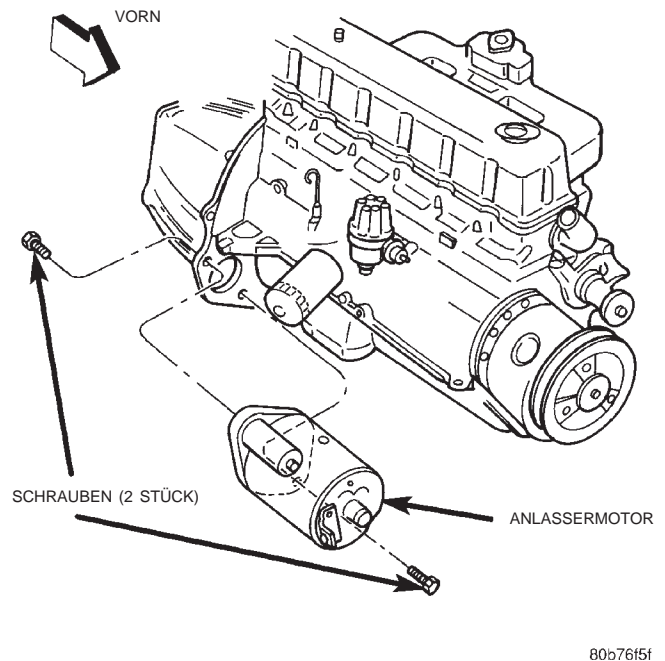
Anlassermotor aus- und einbauen—4.0L-Motor
